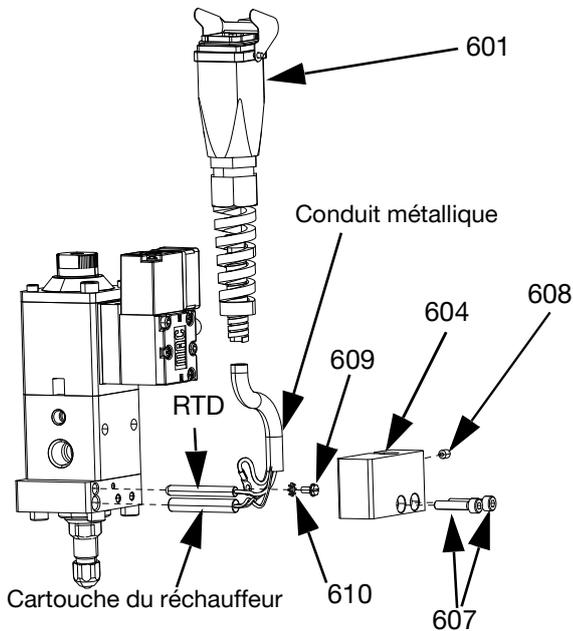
Ensemble réchauffeur pour un bloc de sortie de 0 mm
